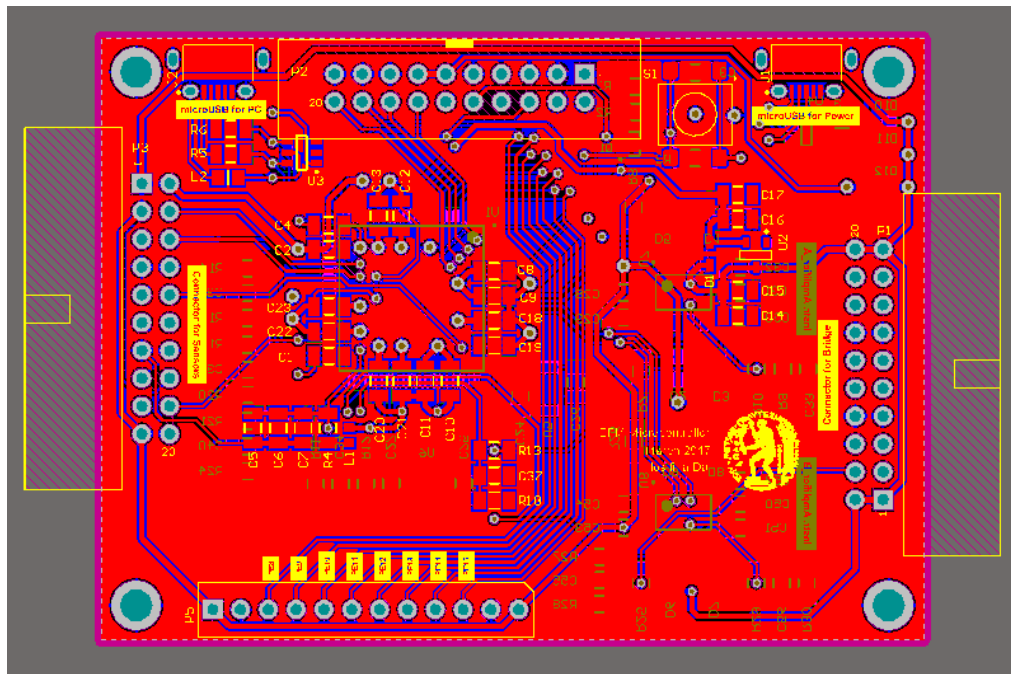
Υλοποίηση PCB πλακέτας μικροελεγκτή
